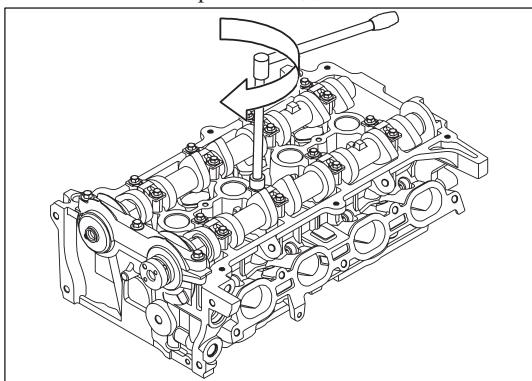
Равномерная затяжка болтов крышек подшипников распределительного вала за два прохода
